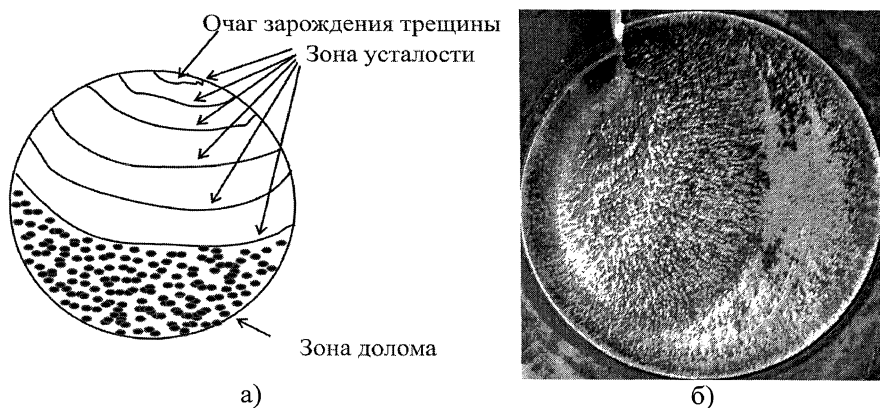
Схема зарождения и развития трещины при переменном изгибе круглого образца (а). Усталостный излом вала (б)
